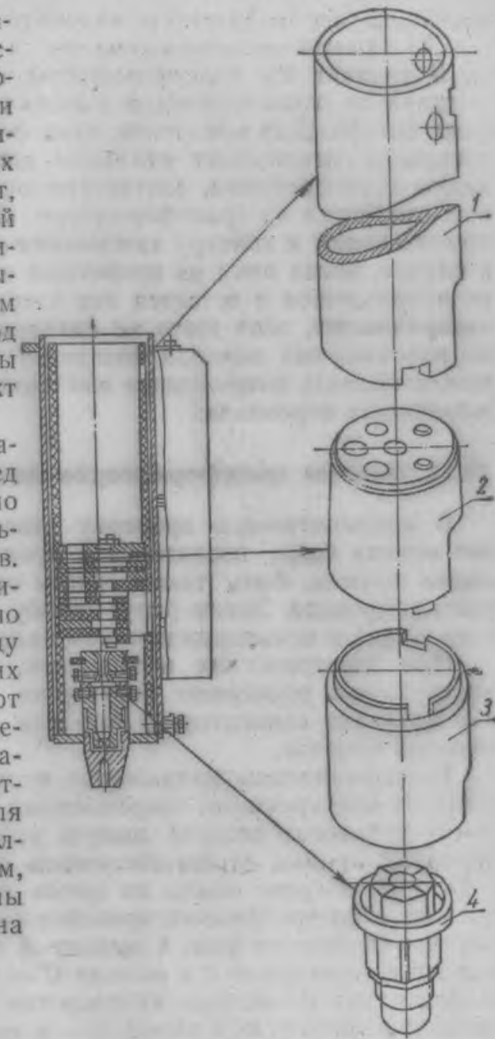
Детали цилиндра выключателя МГГ-10
